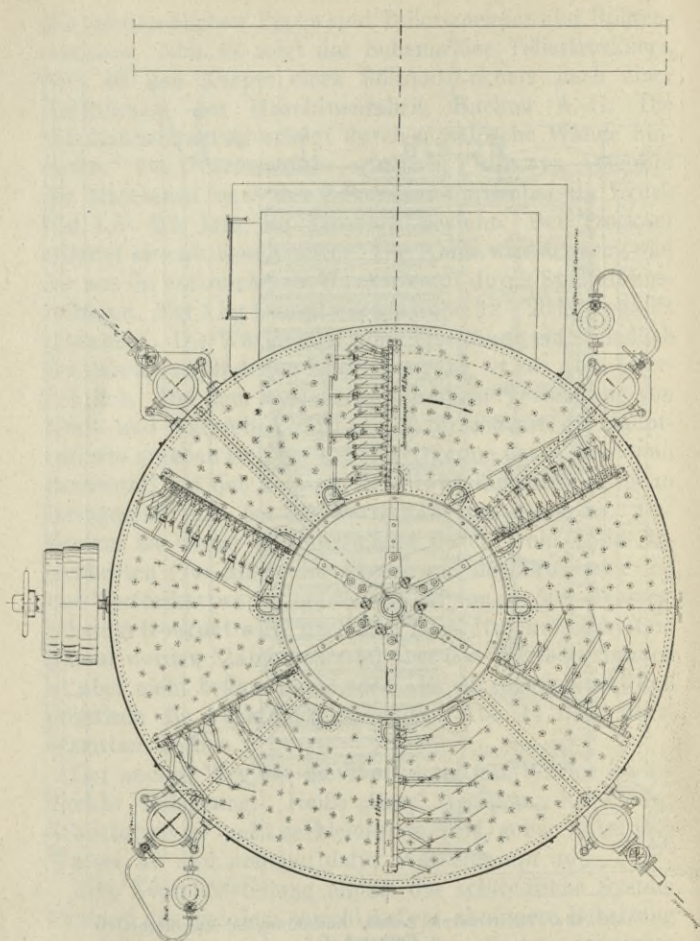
b. Tellertrockner, Grundriß. Ausführung der Maschinenfabrik Buckau A.-G
